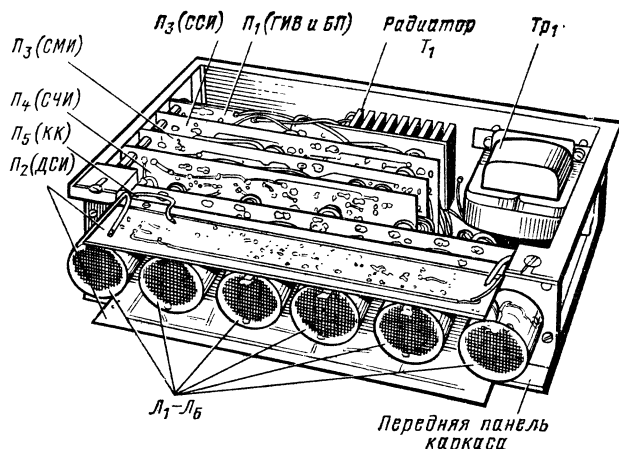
Расположение деталей и печатных плат внутри корпуса.
